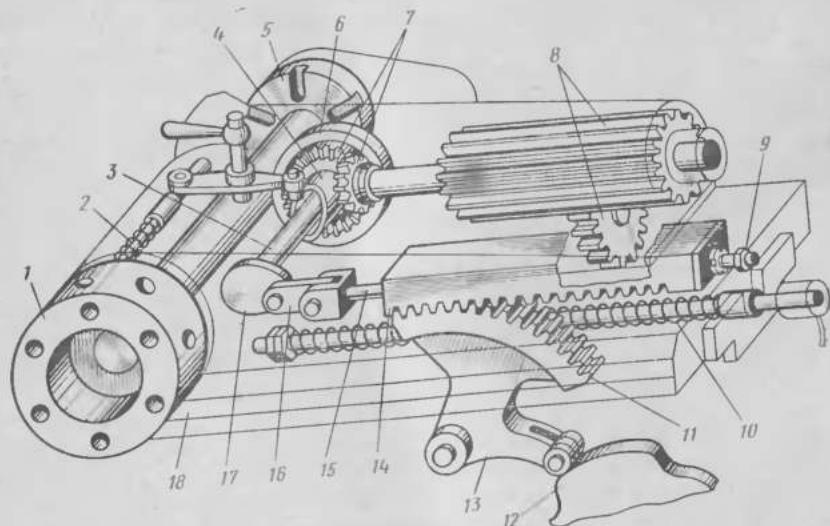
Револьверный суппорт токарно-револьверного автомата
